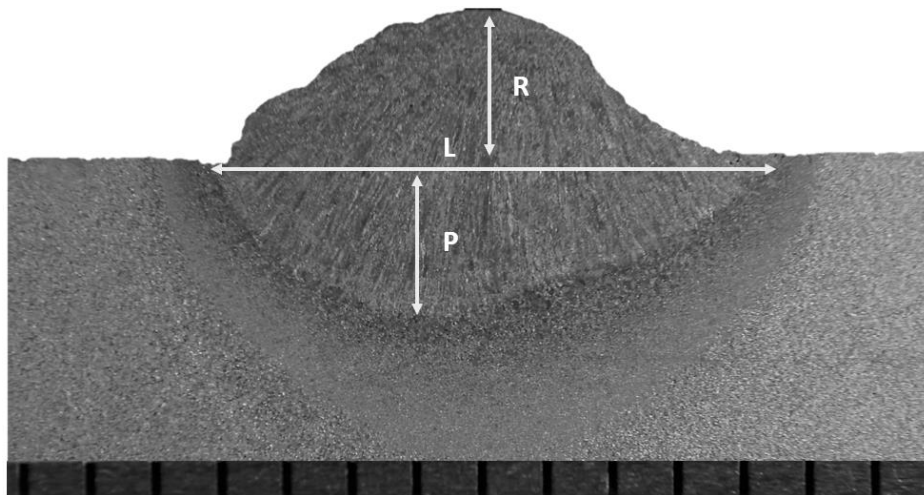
Morfologia do Cordão de solda, R= Reforço; L= Largura, P= Penetração.
